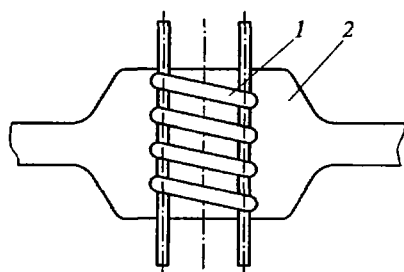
Внутренний спиральный сваривающийся холодильник:
